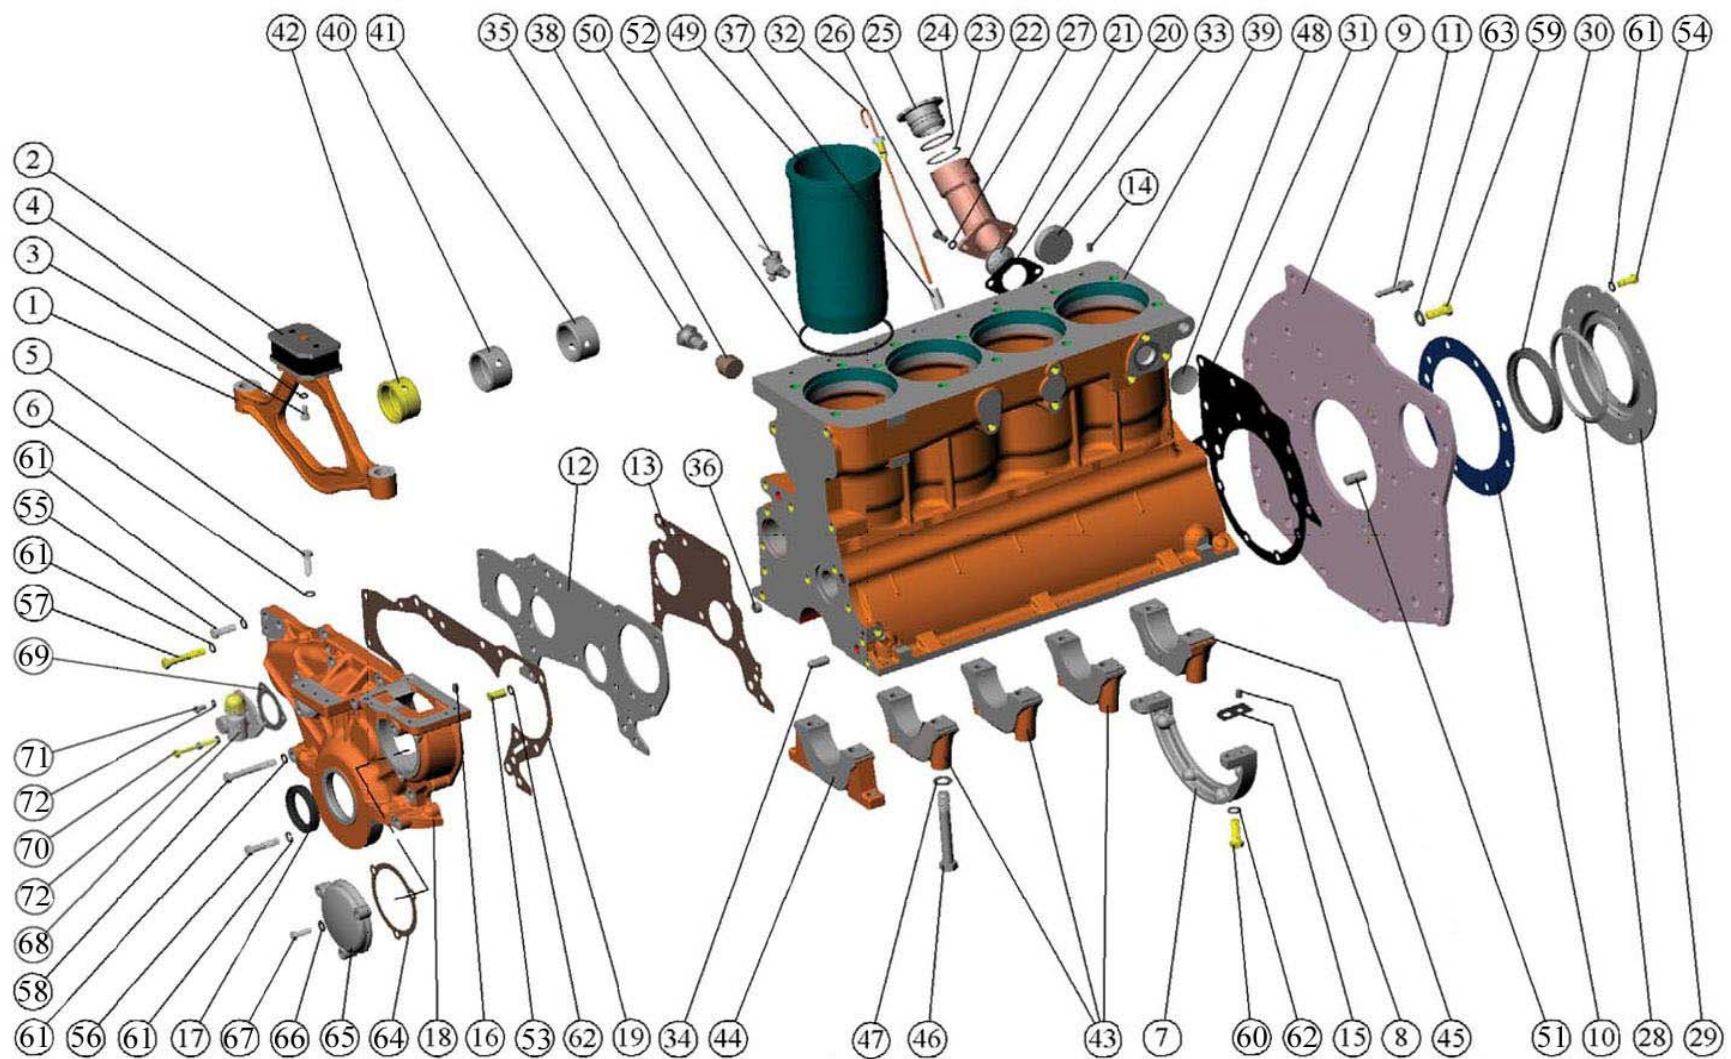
Установка передней опоры. Блок цилиндров. Установка привода и счетчика
